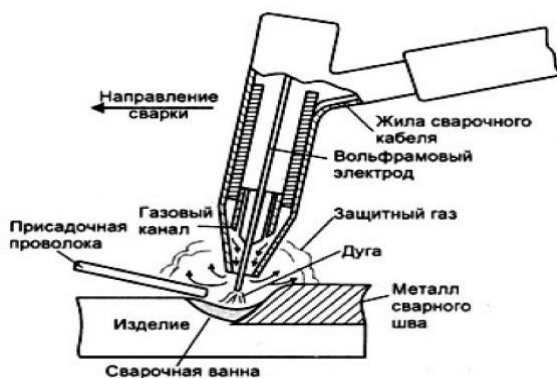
Эскиз аргонодуговой сварки
